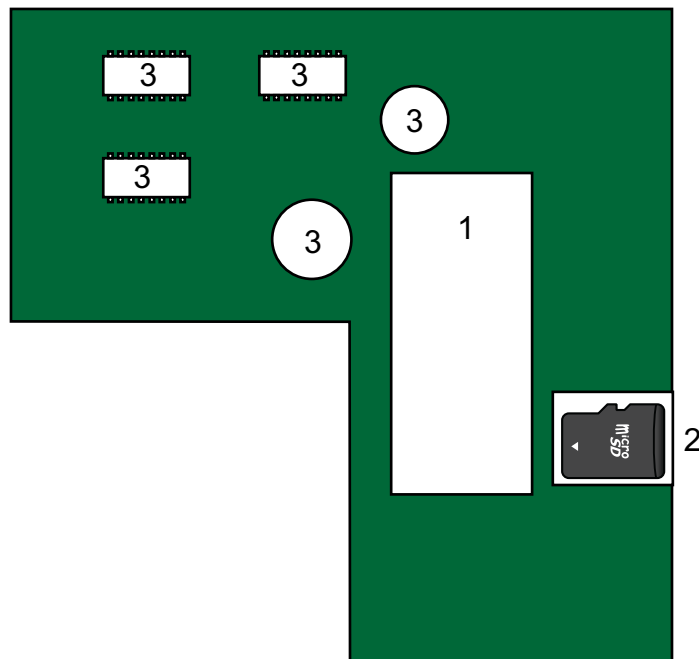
Vista genérica de la PCB principal de la serie PACE E
